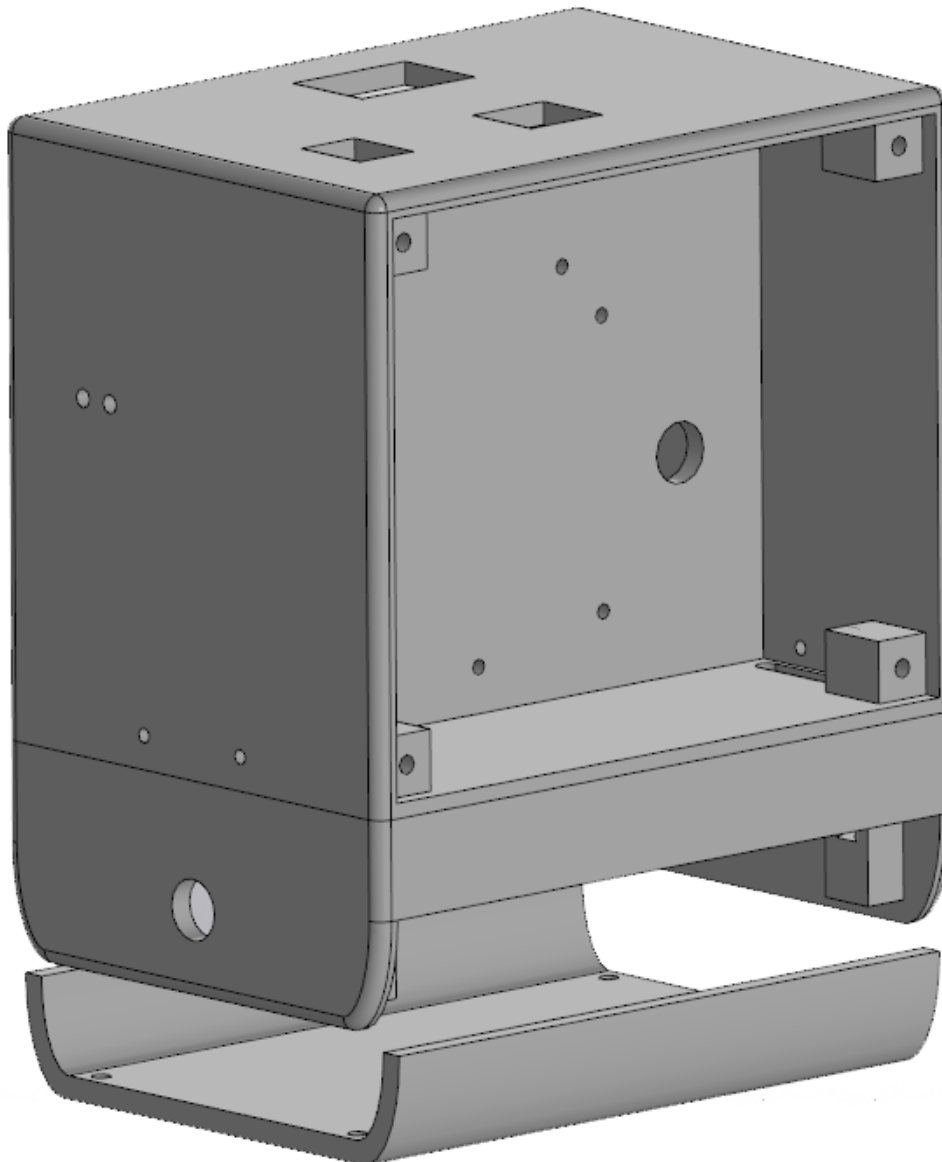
3D-модуль зібраного корпусу робота
